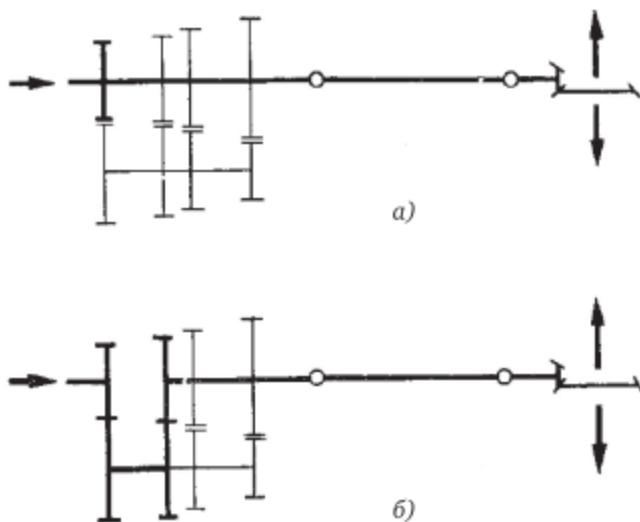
Схема передачи крутящего момента в 3-вальных коробках передач:
